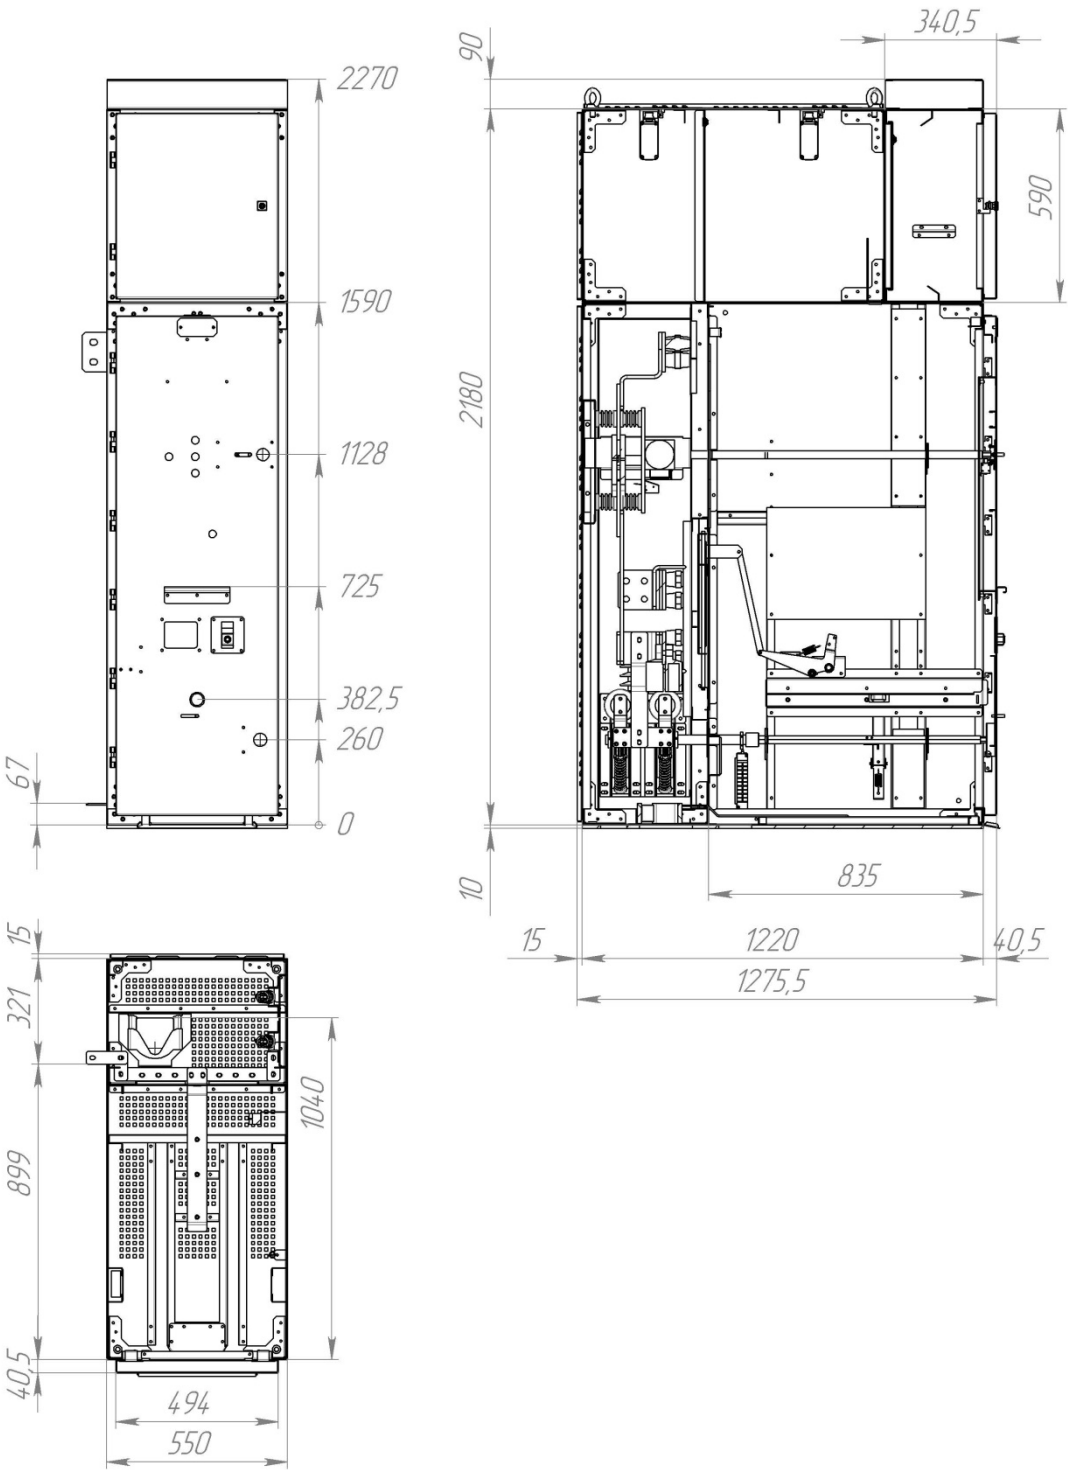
Габаритные и присоединительные размеры КРУ-600В ИРИС
